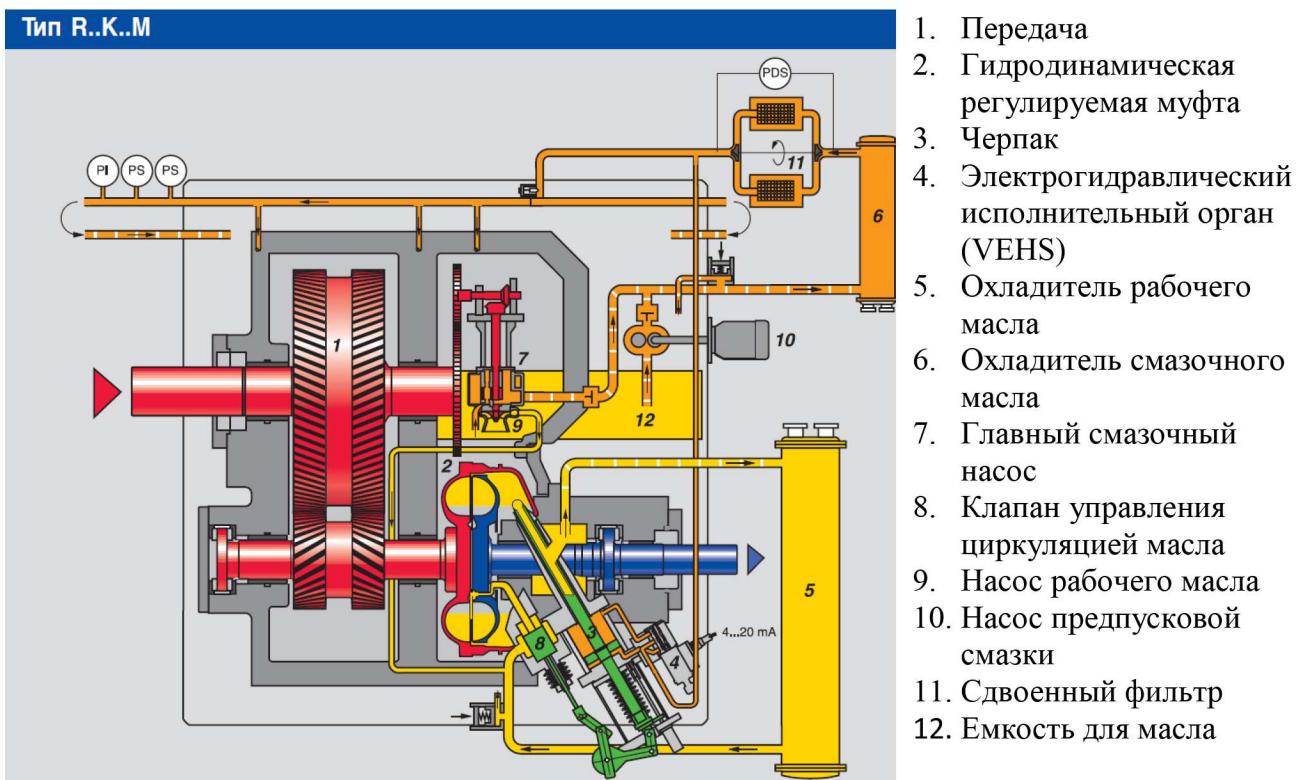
Регулируемая редукторная муфта типа R.K.M
